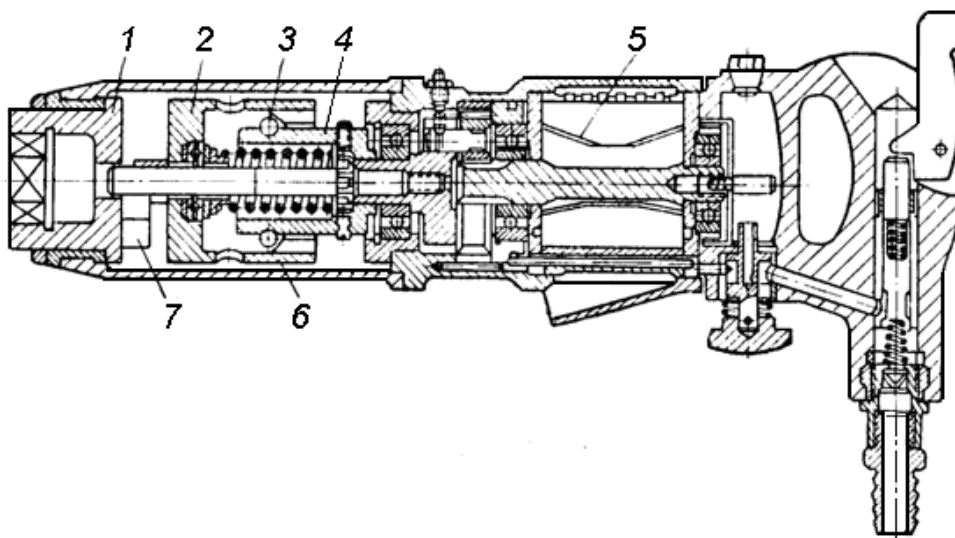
Пневматичний інерційно-ударний гайковерт І-51А
